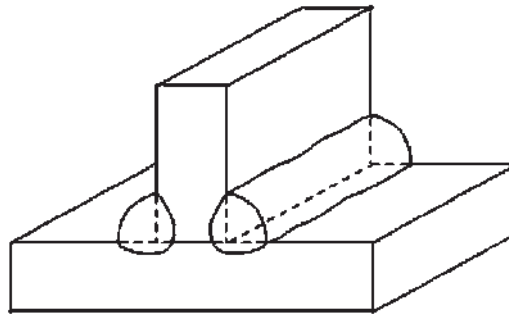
Configuración de las probetas soldadas con junta en T.
